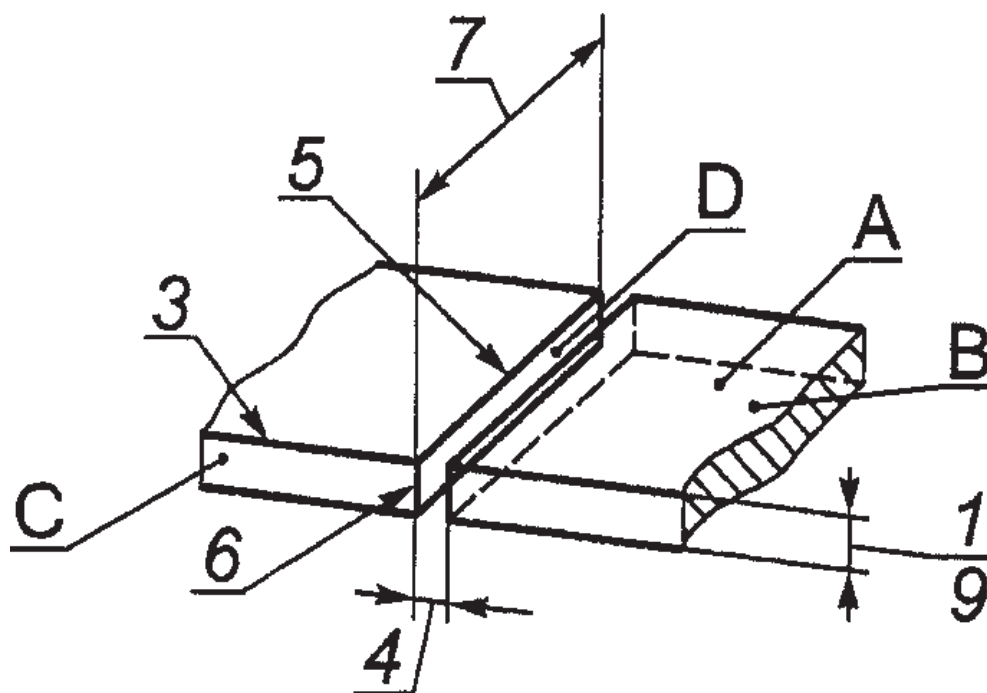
Подготовка под сварку стыкового соединения без скоса кромок Figure 2. Preparation for square butt weld Figure 2.
